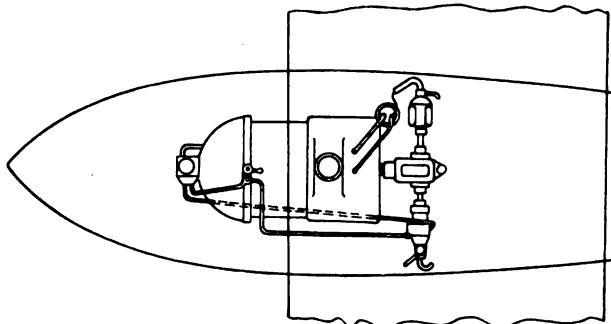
Draufsicht auf den Dampferzeuger im Rumpf
